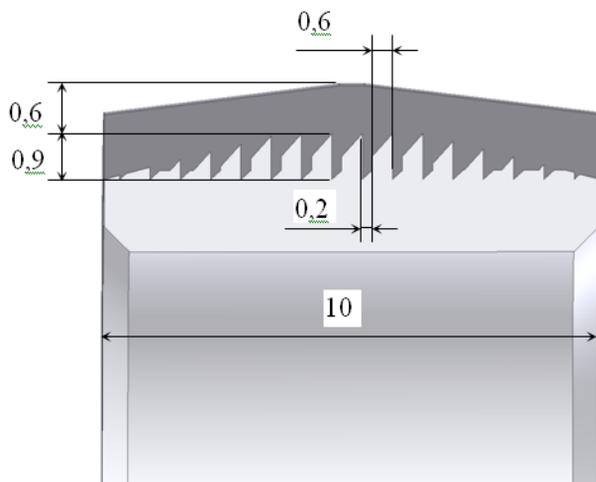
Схема рабочего кольца с твердосплавным покрытием
